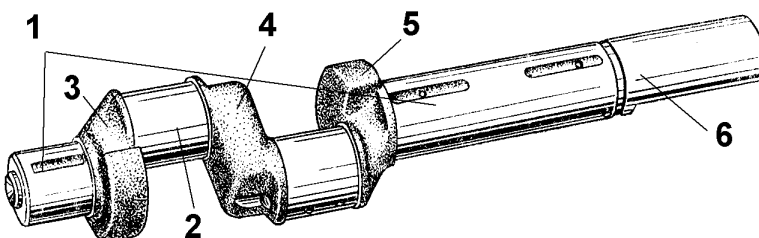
Двоопорний двоколінчастий вал безсальникового компресора:
